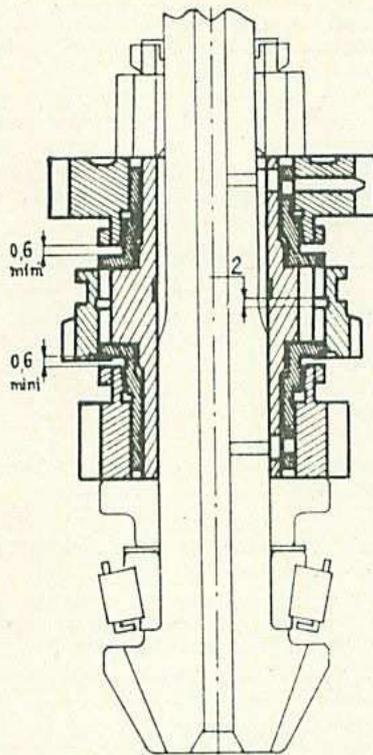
Vue en coupe de l'arbre pignon d'angle (boîte CS).
